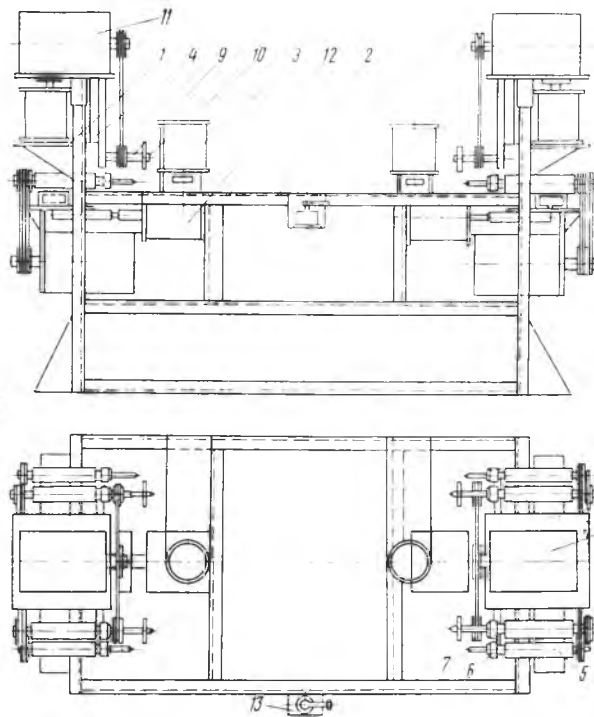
12-шпиндельный сверлильно-прорезной станок
